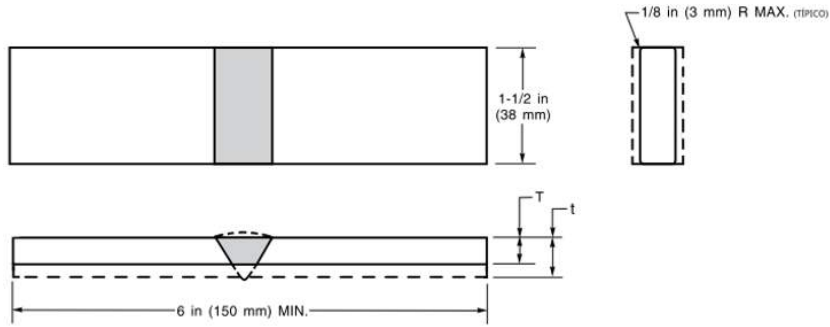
Dimensiones de probetas para doblado de cara
